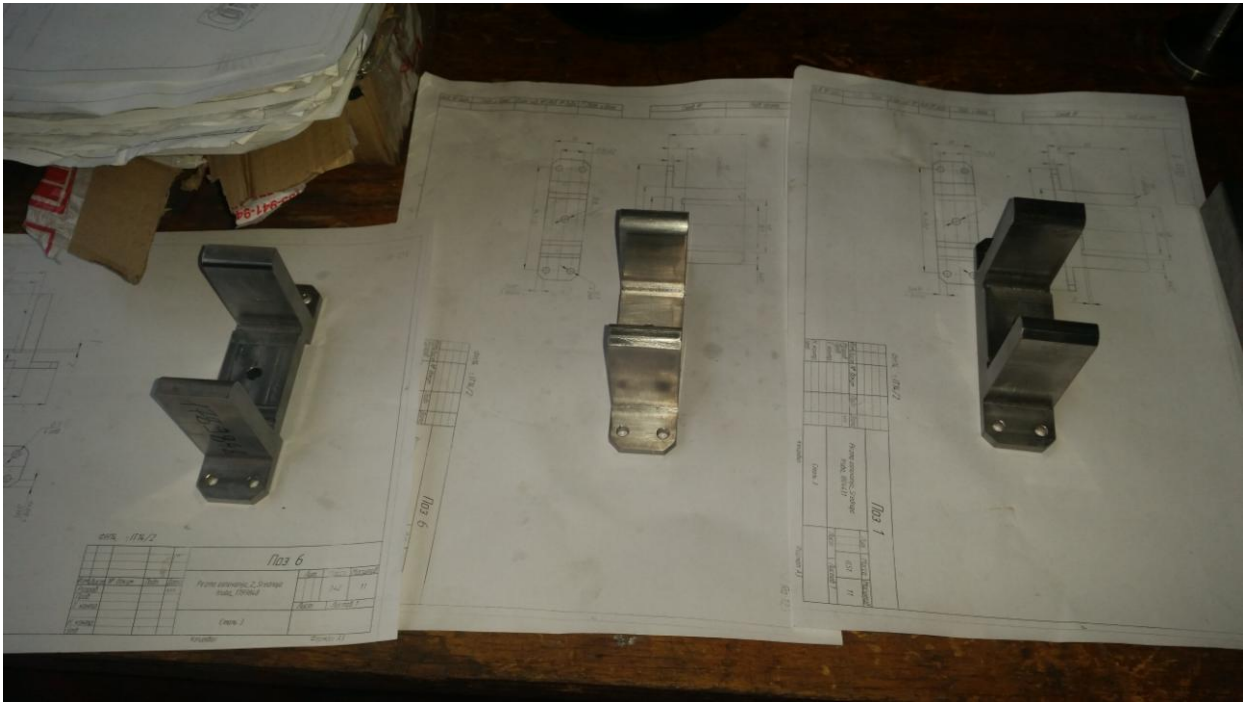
Изготовленные с помощью фрезерного обрабатывающего центра малоразмерные корпусные детали
